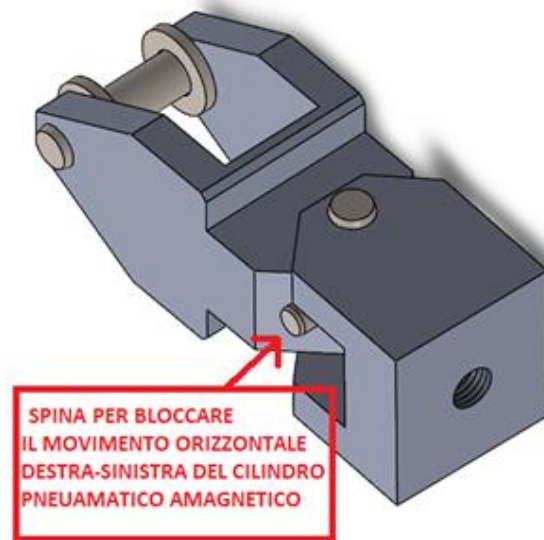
Assemblaggio dei due perni a forcetta e spina per bloccare il movimento orizzontale destra-sinistra del cilindro pneumatico
